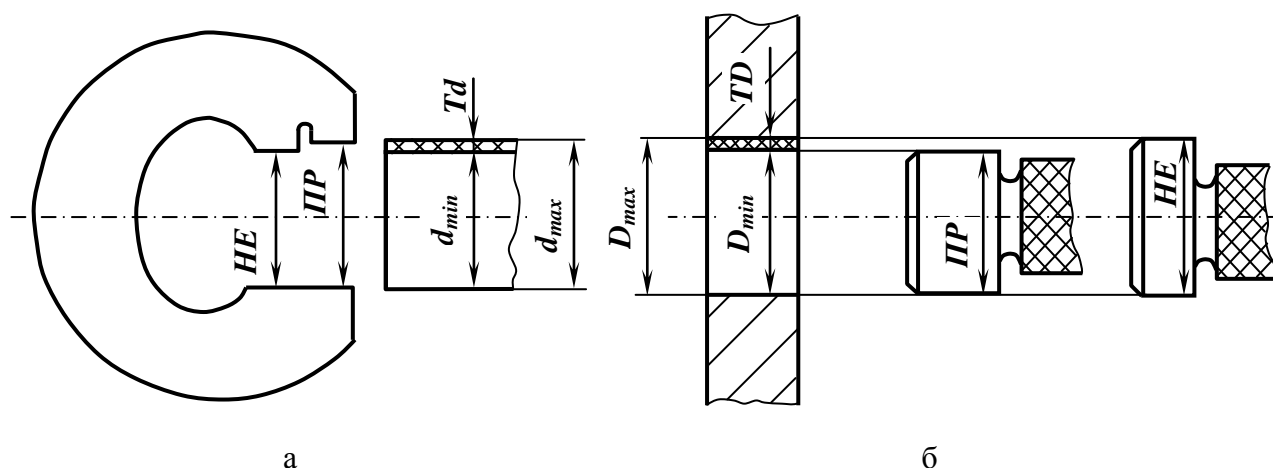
Схемы контроля деталей: а – вала скобой; б – отверстия пробками
